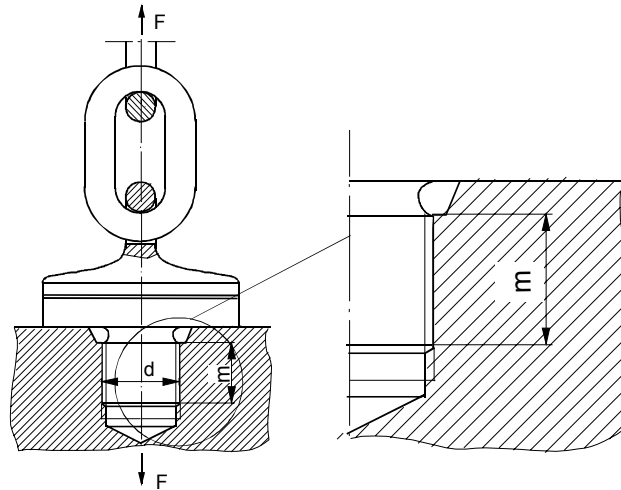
Wälzgelagerter Wirbelblock mit Einschraubverbindung
